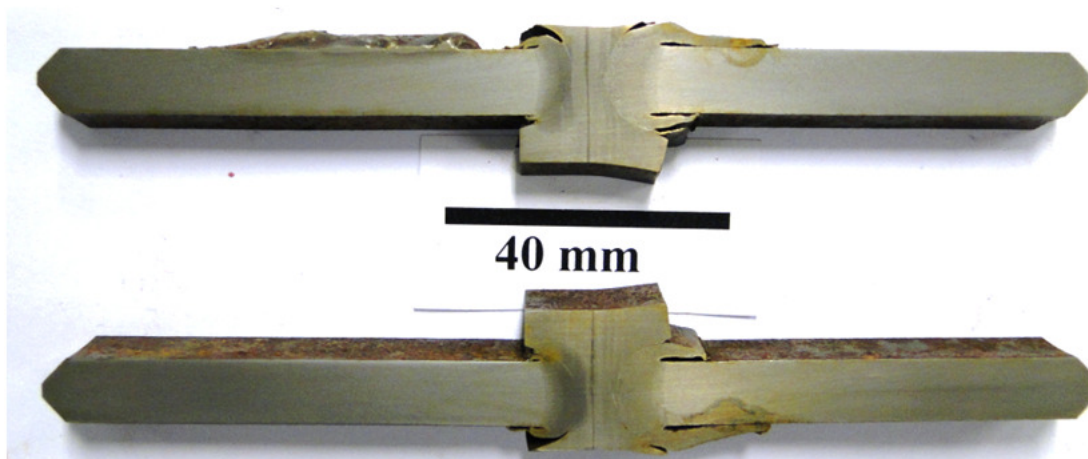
Macrografia do perfil de soldagem entre tubo-anel-tubo.
